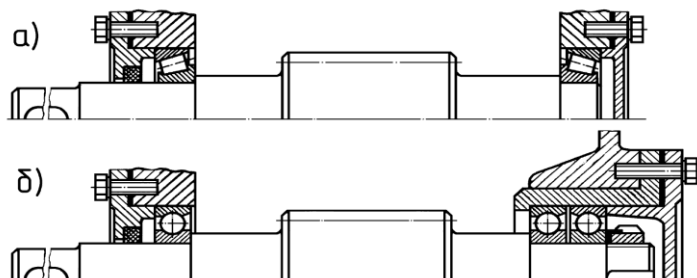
Схема опорних вузлів вала черв'яка:
